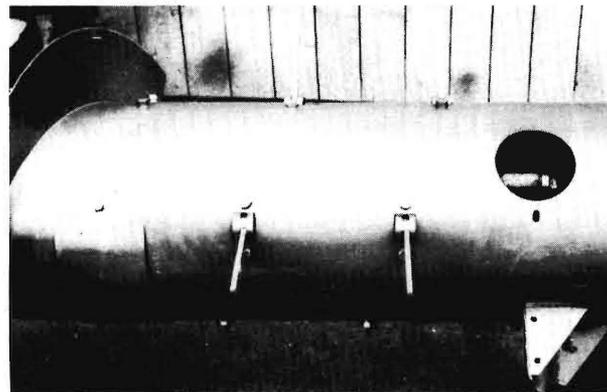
Übliche Fronteingzugsschnecke aus einem geschlossenen Blechzylinder mit aufgeschweissten Schneckengängen und zurückziehbaren Fingern.
